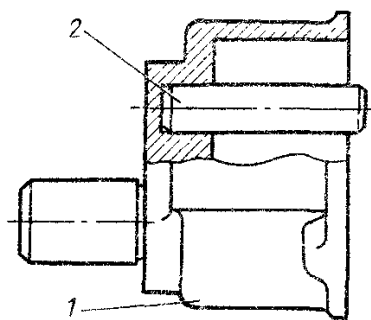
Корпус масляного насоса с осью ведомой шестерни в сборе:
